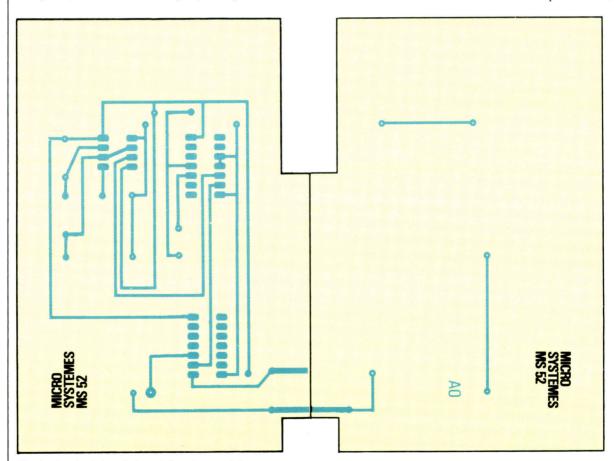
Le circuit imprimé vu côté soudure et côté composants.
